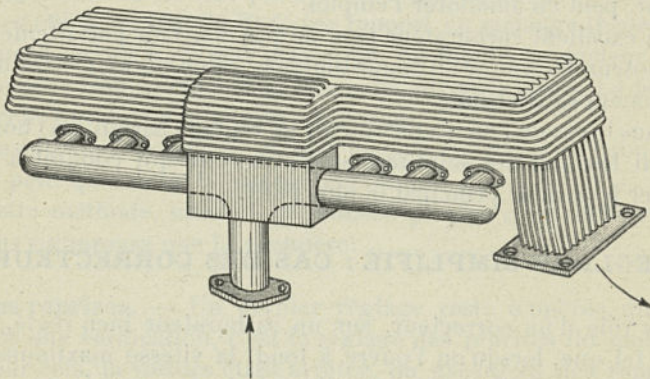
Dessin moderne de collecteurs (6 cylindres).
